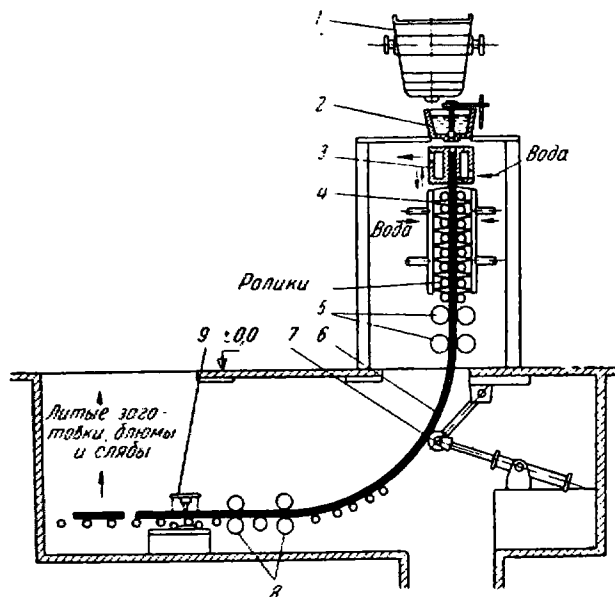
Схема установки для непрерывной разливки стали (УНРС):
